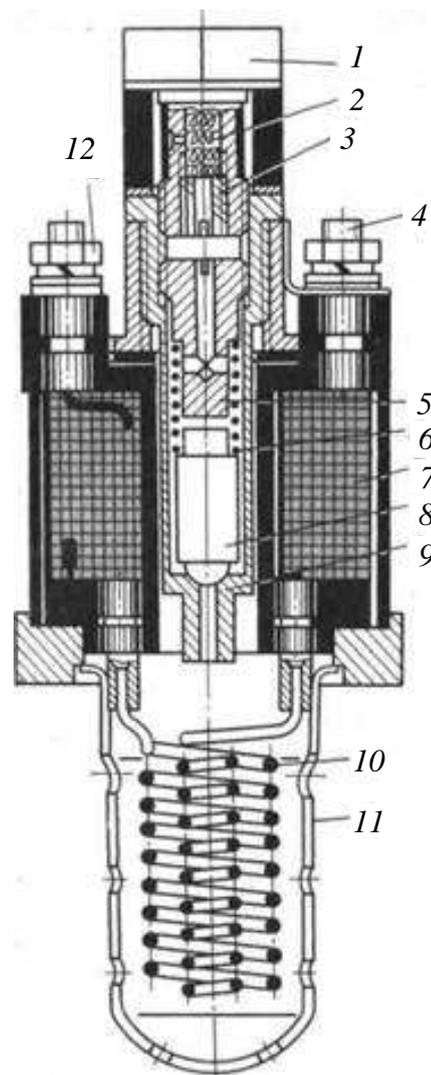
Электрофакельный подогреватель: 1 – болт штуцера; 2 – дозирующий элемент; 3 – гайка; 4 – токоподводящая клемма спирали; 5 – штуцер; 6 – пружина перепускного клапана; 7 – катушка электромагнита; 8 – клапан; 9 – корпус клапана; 10 – спираль; 11 – кожух; 12 – токоподводящая клемма катушки электромагнита
